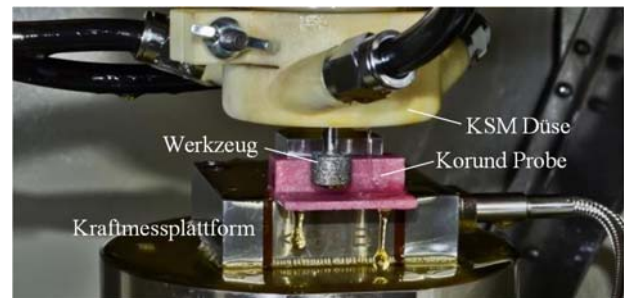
Versuchsaufbau für Abrichtversuche mit touchierten Diamantwerkzeugen.
